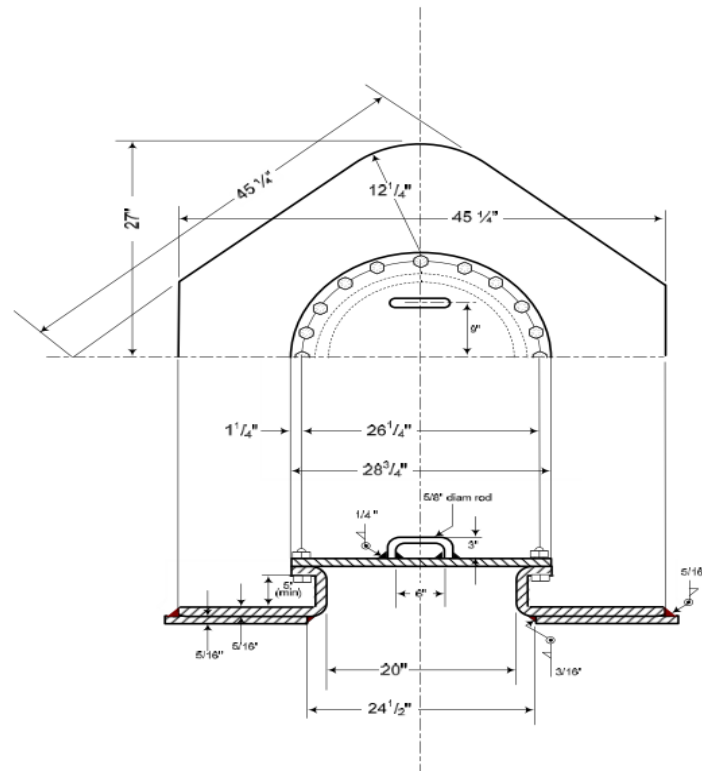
Detail untuk *flange and bolt* pada *head* reaktor
